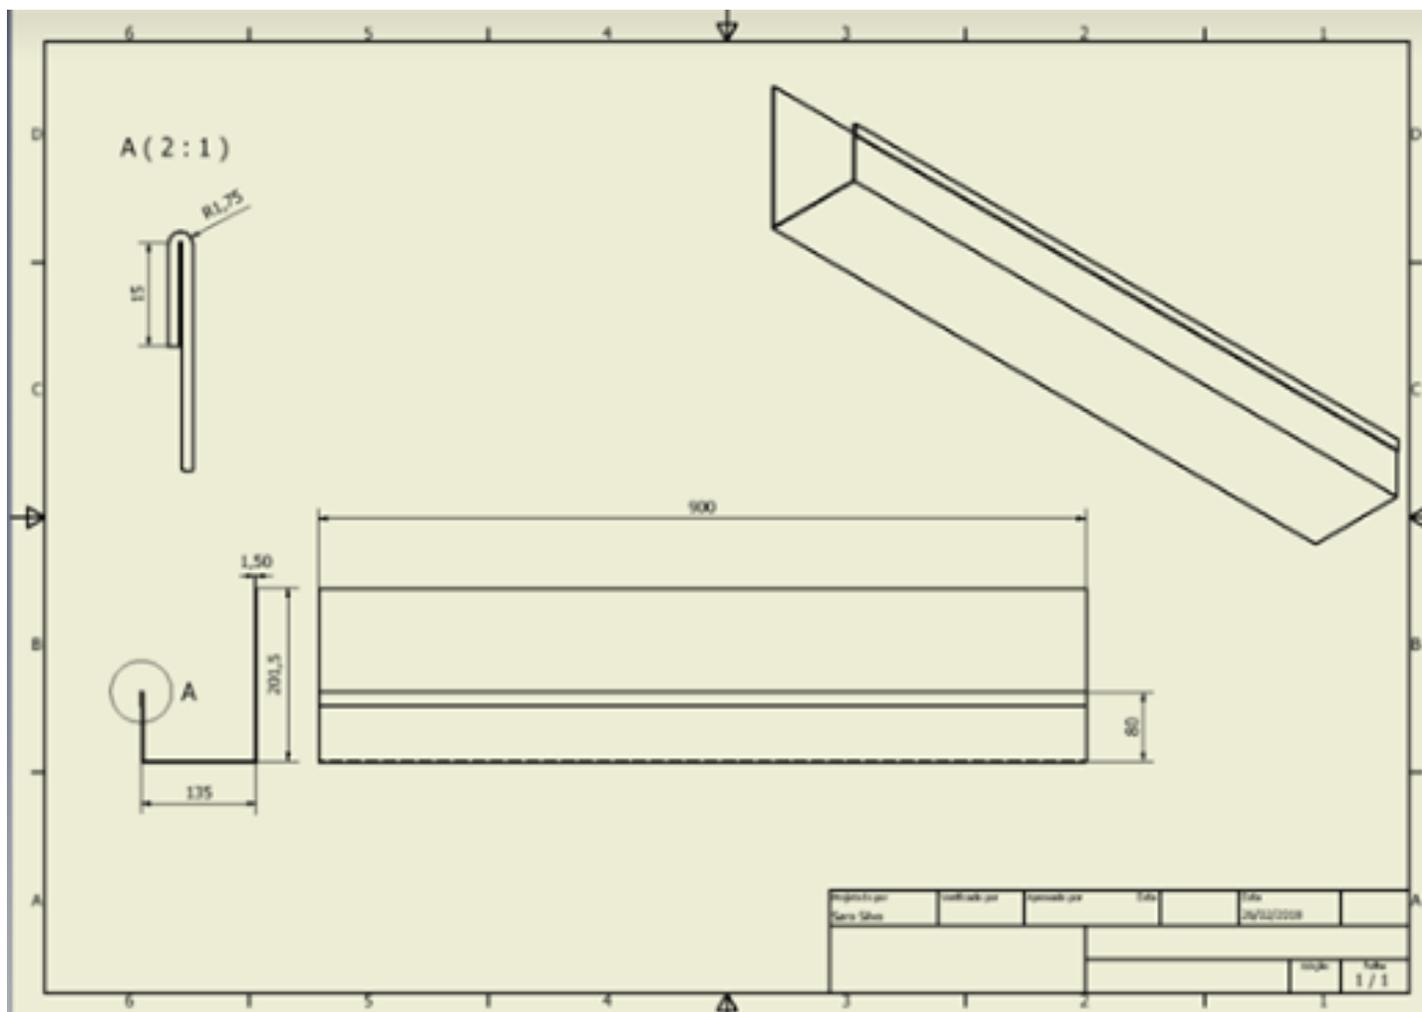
Desenho técnico para caixa de suporte de ferramentas e utensílios
